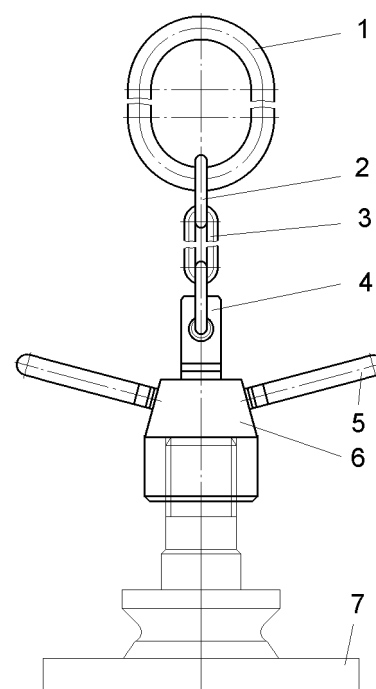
Чалочное приспособление для транспортировки цилиндра подвески:
